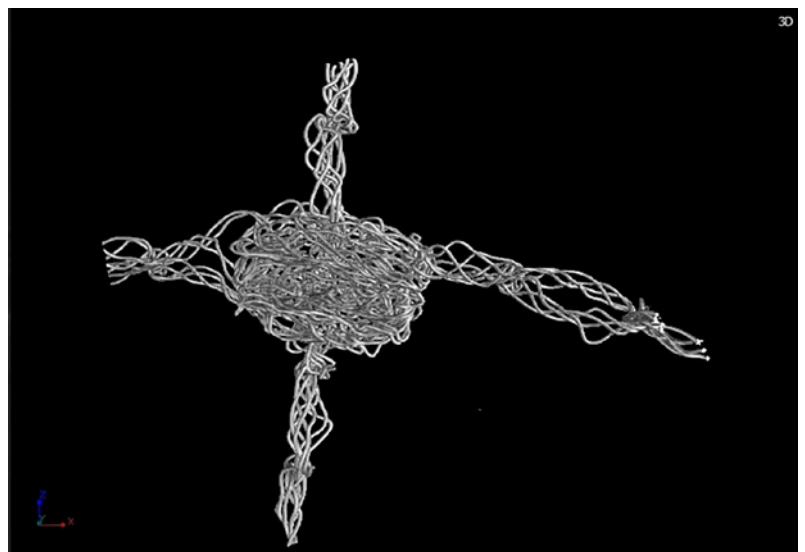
CT-Aufnahme eines ultraschallgeschweißten Kontaktes
